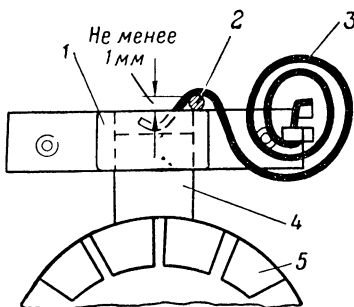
Схема проверки зазора между щеткодержателем стартера и пружинной щеткодержателя:
